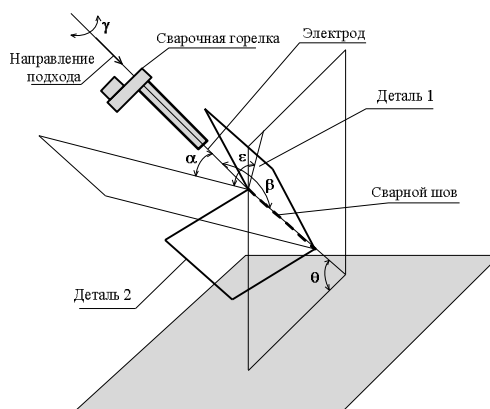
Ориентация горелки дуговой сварки и сварного шва
